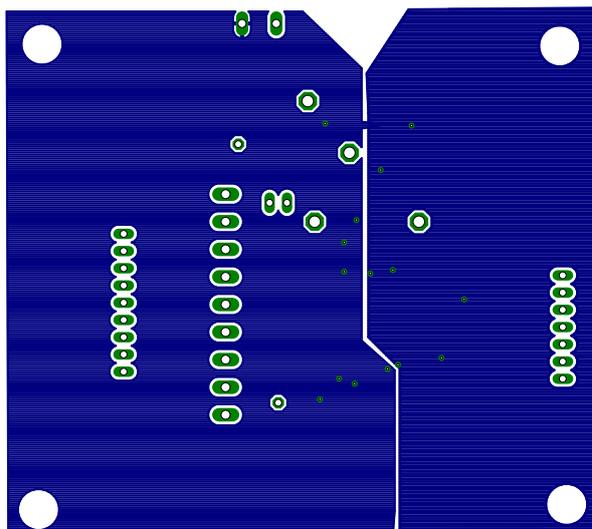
Capa inferior del PCB de la primer versión: *BOTTOM
